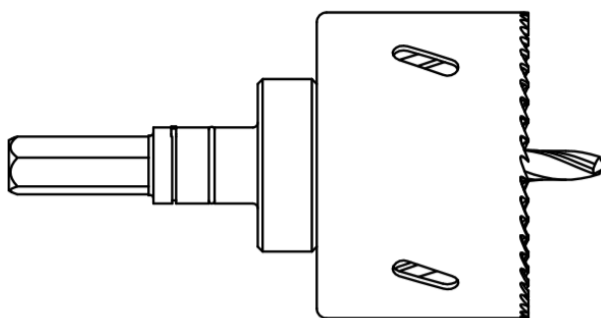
Біметалічне Корончасте свердло фірми BOSCH
